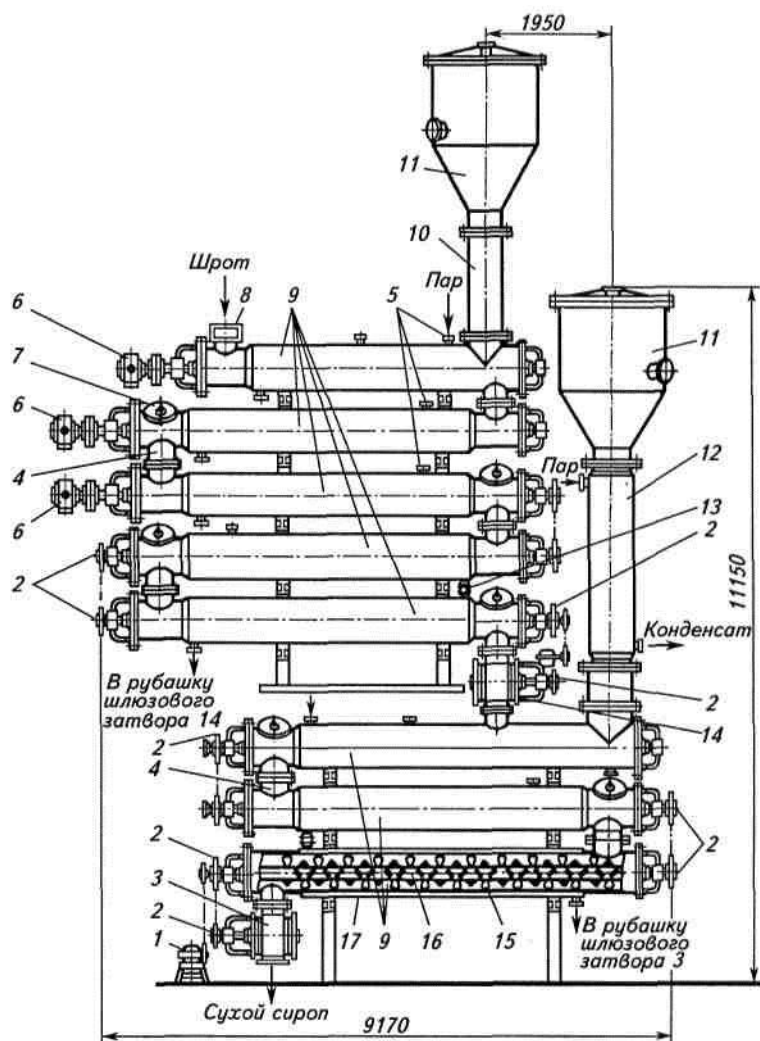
Модернизированный шнековый испаритель: 1 — лубрикатор; 2 — цепные передачи; 3, 14 — шлюзовые затворы; 4 — перепускной патрубок; 5, 13 — патрубки для подвода глухого водяного пара; 6 — электродвигатели; 7 — люк-лаз; 8 — патрубок для ввода шрота в испаритель; 9 — испарительные шнеки; 10, 12 — паровые трубы; 11 — сухие шротоловушки; 15 — лопатки; 16 — полый вал; 17 — паровая рубашка.
